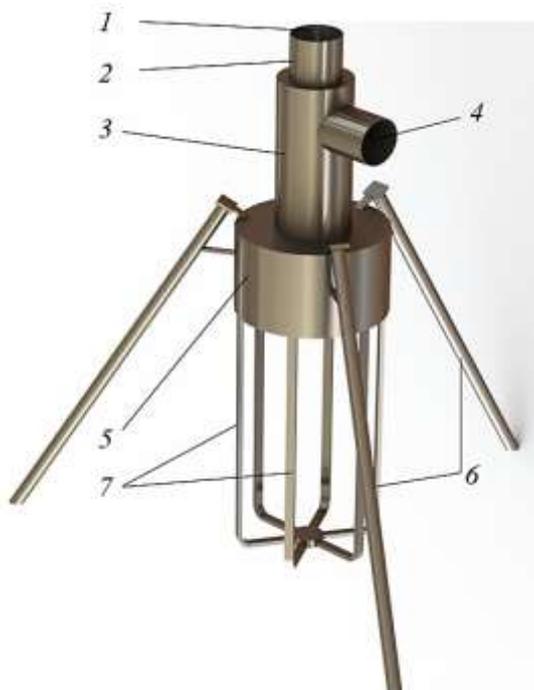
Трехмерная модель мультивихревого классификатора: 1 – входной патрубок, 2 – внутренняя цилиндрическая труба, 3 – внешняя цилиндрическая труба, 4 – выходной патрубок, 5 – цилиндрическая часть, 6 – опоры, 7 – металлическая конструкция для съемной емкости
